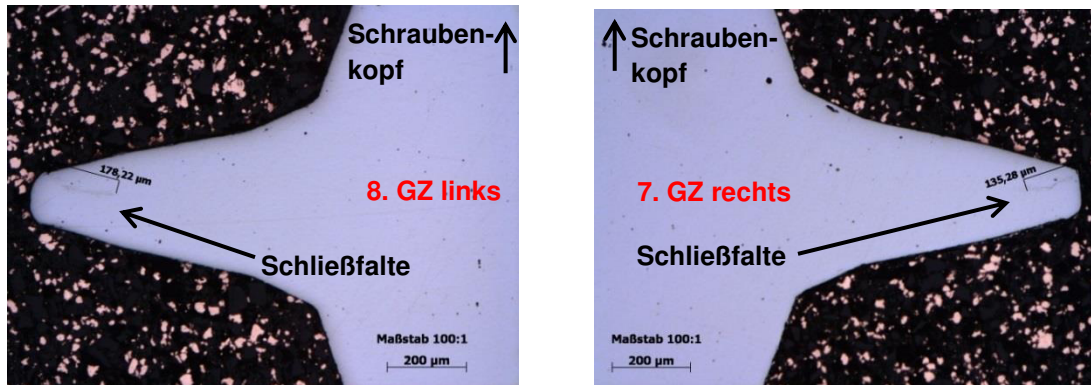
Schließfalte bei einer korrekt ausgewalzten Schraube (GZ= Gewindegang)
